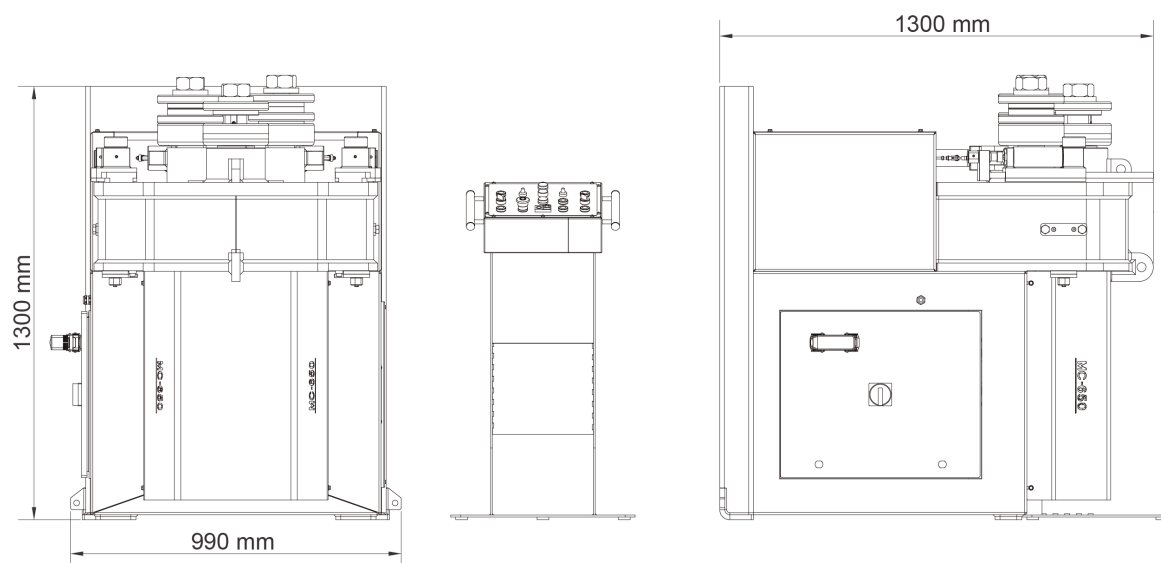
Dimensions de la machine avec le bâti en position horizontale
